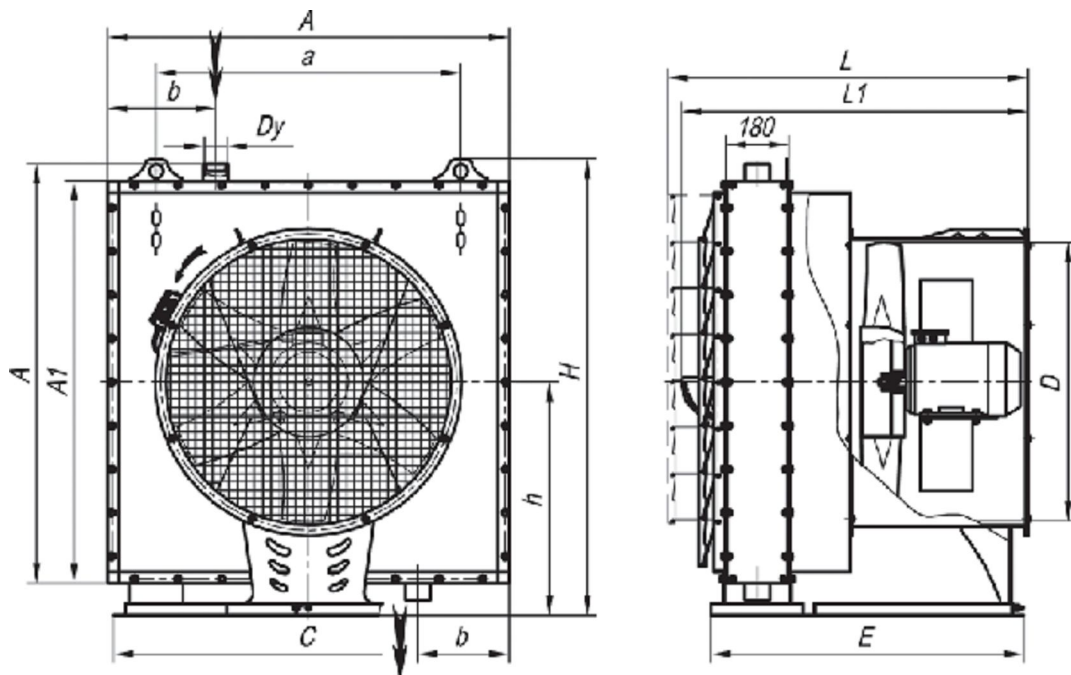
Габаритные и присоединительные размеры агрегатов воздушно-отопительных АО2 №3-6,3Г на базе воздухонагревателей типа КП.
